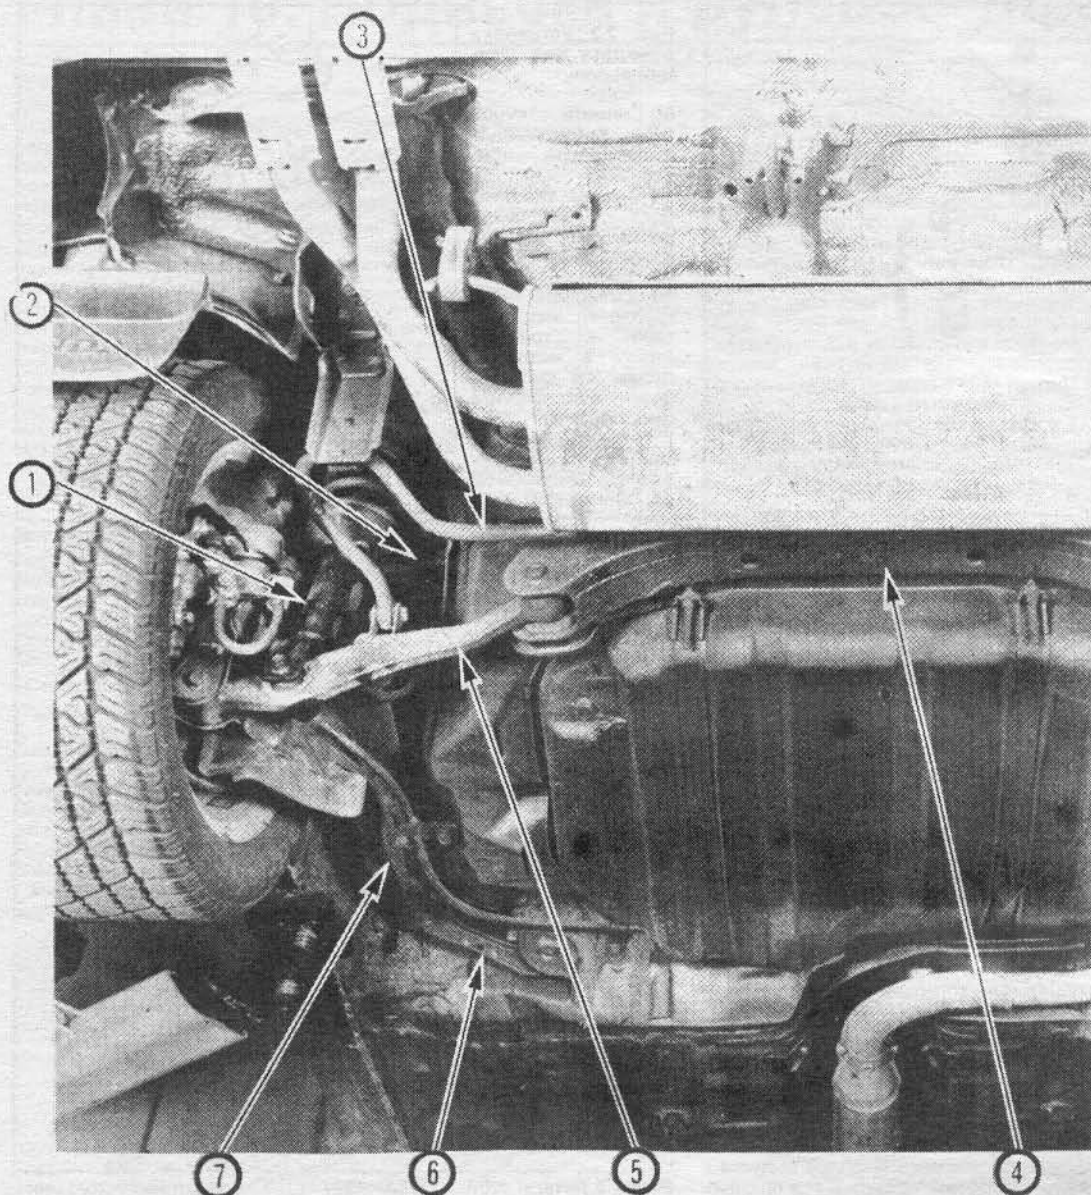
Задняя подвеска с 1988 года: 1 - амортизатор; 2 - верхний рычаг; 3 - стабилизатор; 4 - поперечина; 5 - компенсационный рычаг; 7 - направляющий рычаг.
